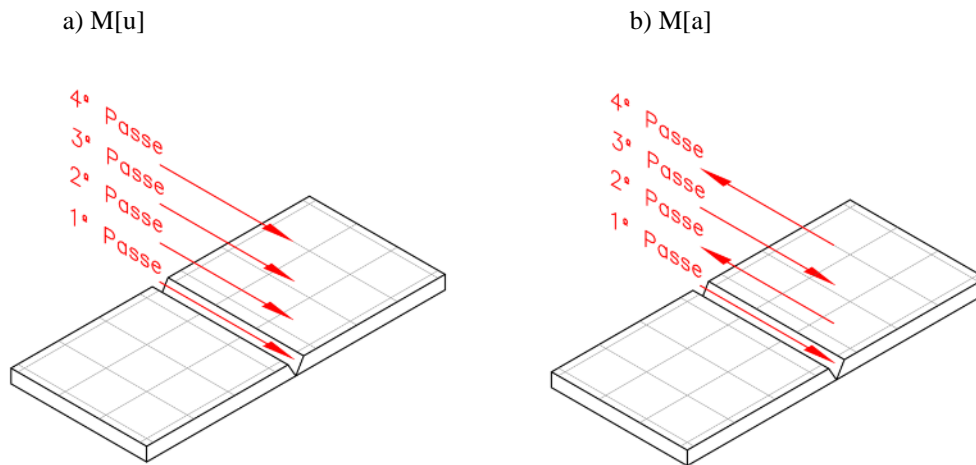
Sequência e sentido de passes a serem executados na soldadura multipasses em juntas de topo
